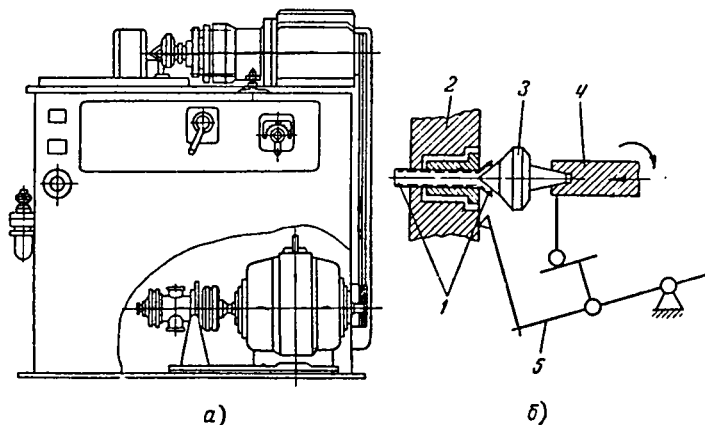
Труборазвальцовочный станок (а), схема развальцовки трубы на нем (б)
